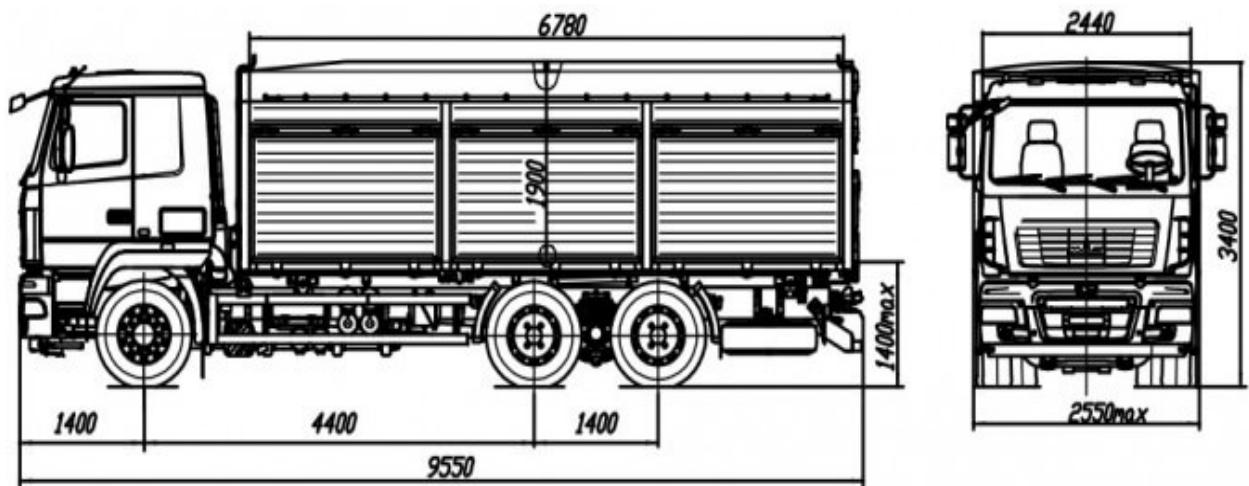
Схема зерновоза МАЗ-6501С9-8525-000 (розроблено за [20])
